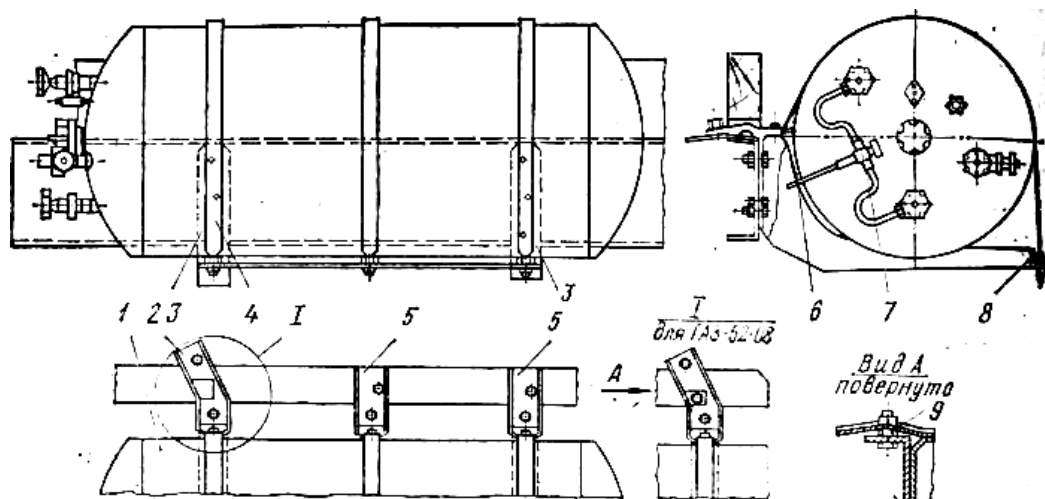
Установка балона на вантажному автомобілі: 1 – балон; 2 – підсилювач поперечний передній; 3 – кронштейни балона; 4 – хомут кріплення балона; 5 – підсилювач поперечний задній; 6 – прокладка хомута; 7 – трійник; 8 кутник; 9 – втулка
